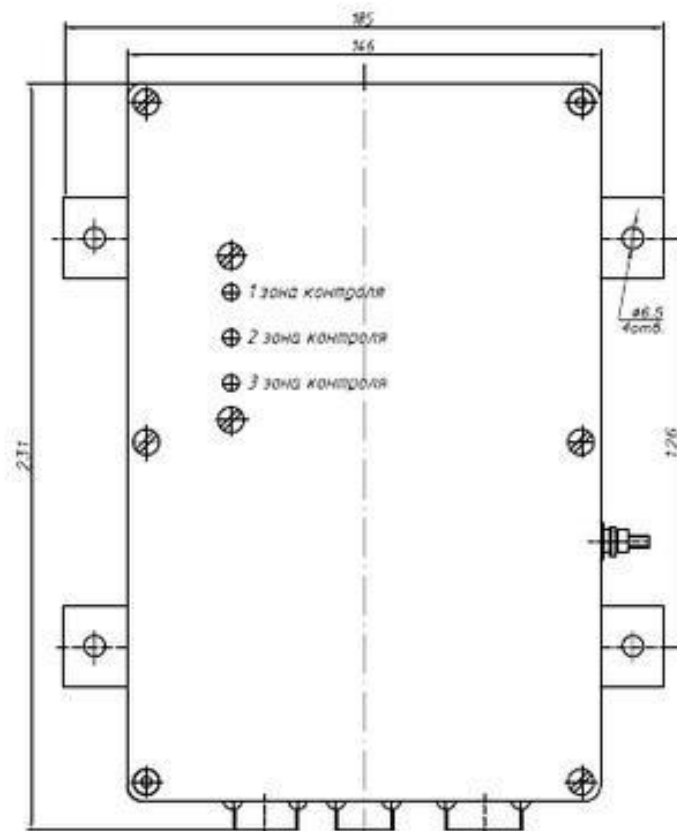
Габаритные и присоединительные размеры ВП МГДУ.
